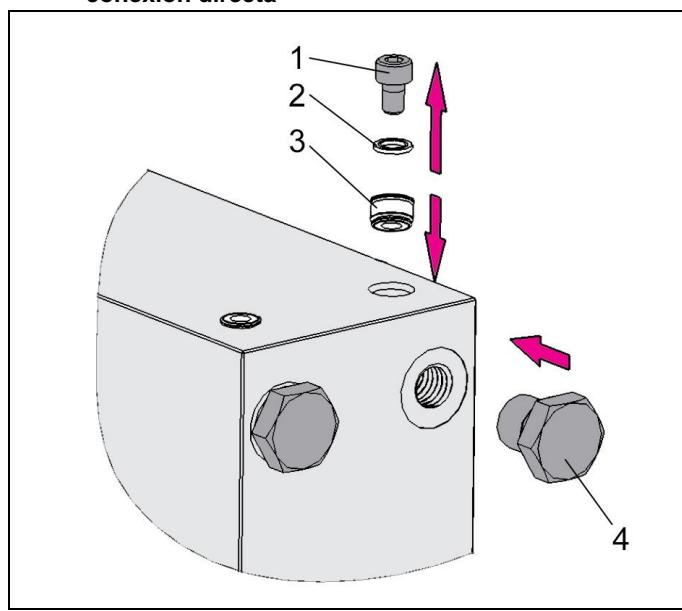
Ejemplo de preparación para conexiones hidráulicas sin tuberías mediante unión enchufable para conexión directa
